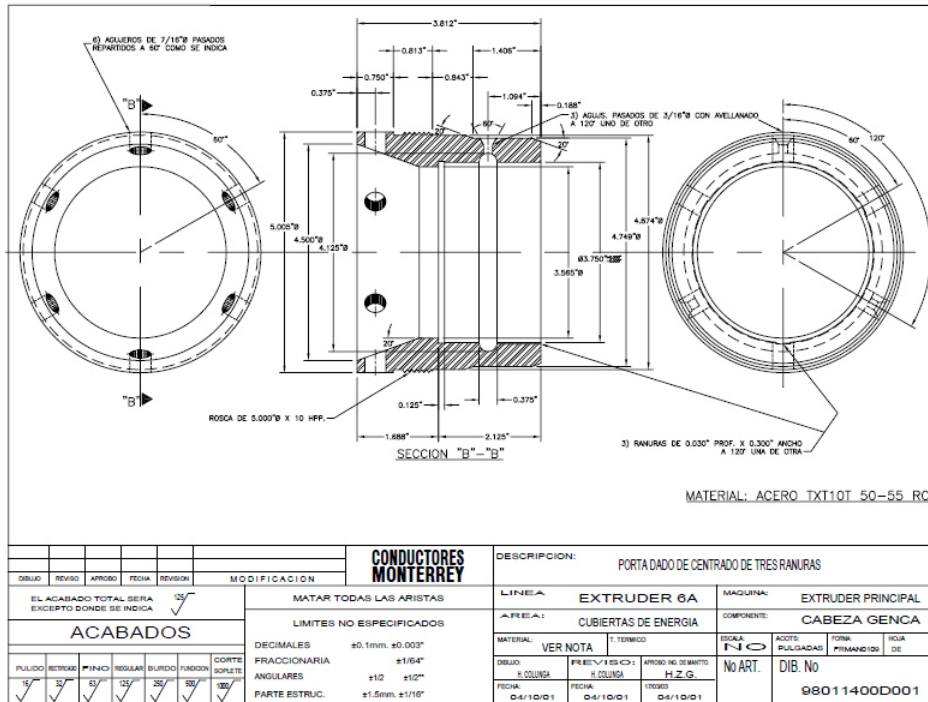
Diseño de porta-dado utilizado en planta Monterrey para aplicación de trazas. [45]
